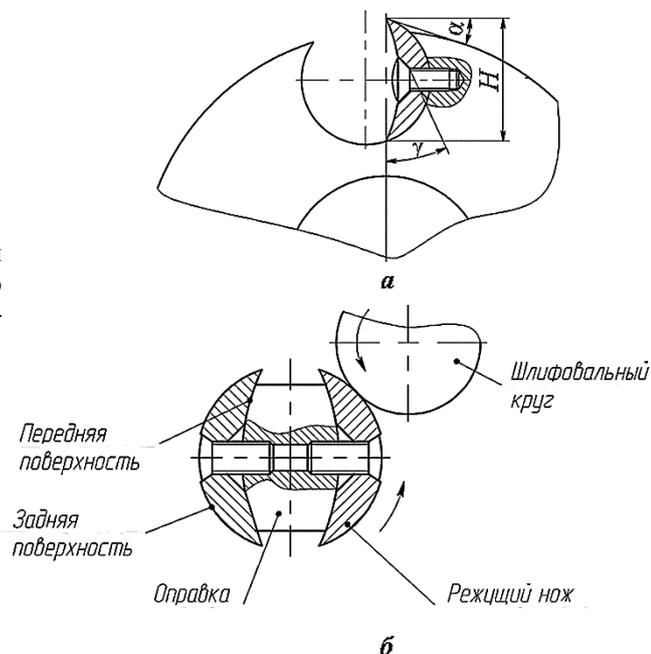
Узел крепления серпообразного режущего элемента (а) и схема заточки ножей по задней поверхности (б)
